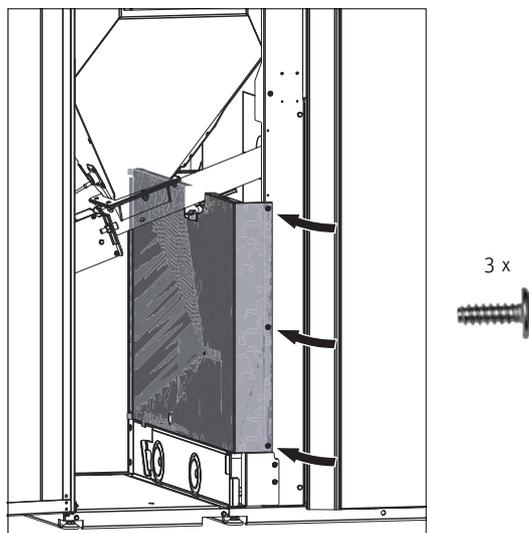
Spingere la piastra di protezione dal contatto dietro e avvitarela anteriormente
